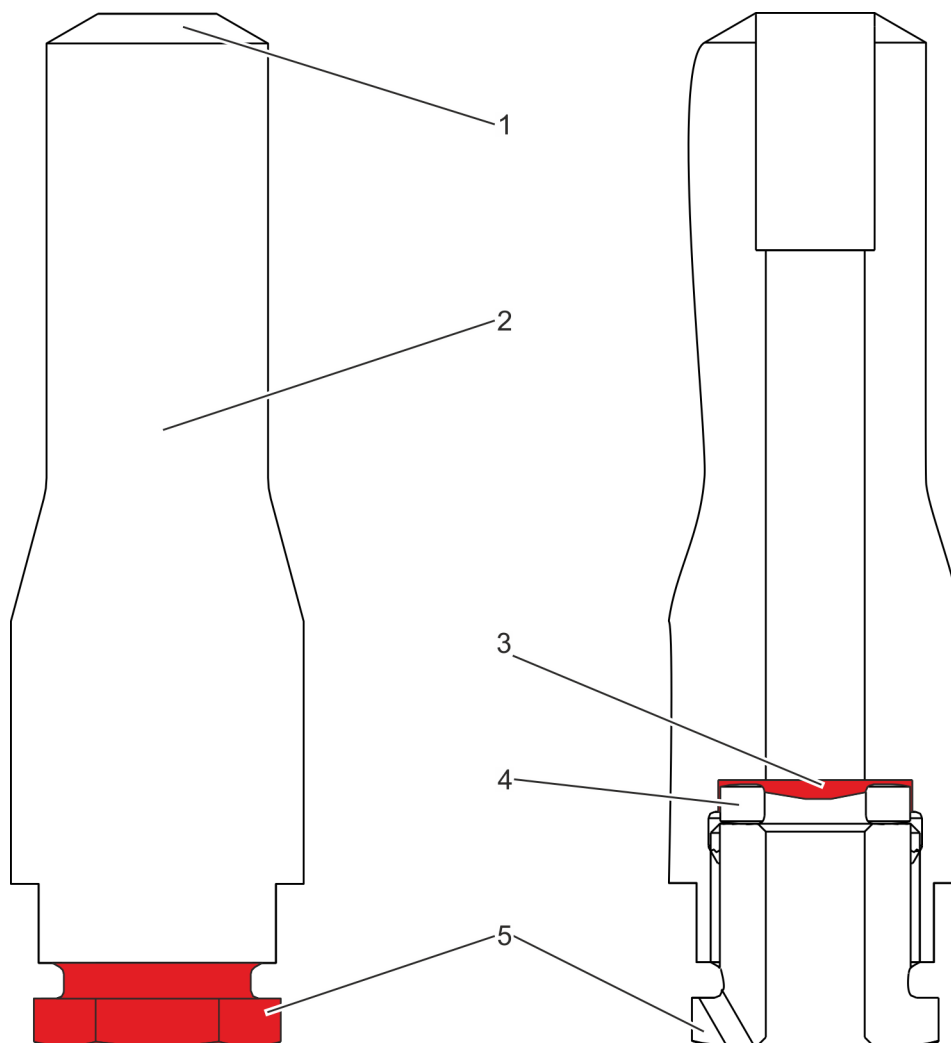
Vue d'ensemble (à gauche) et vue en coupe (à droite)
